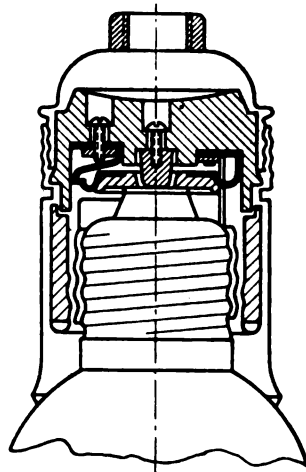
„Elt“-Fassung mit eingeschraubter Glühlampe.
